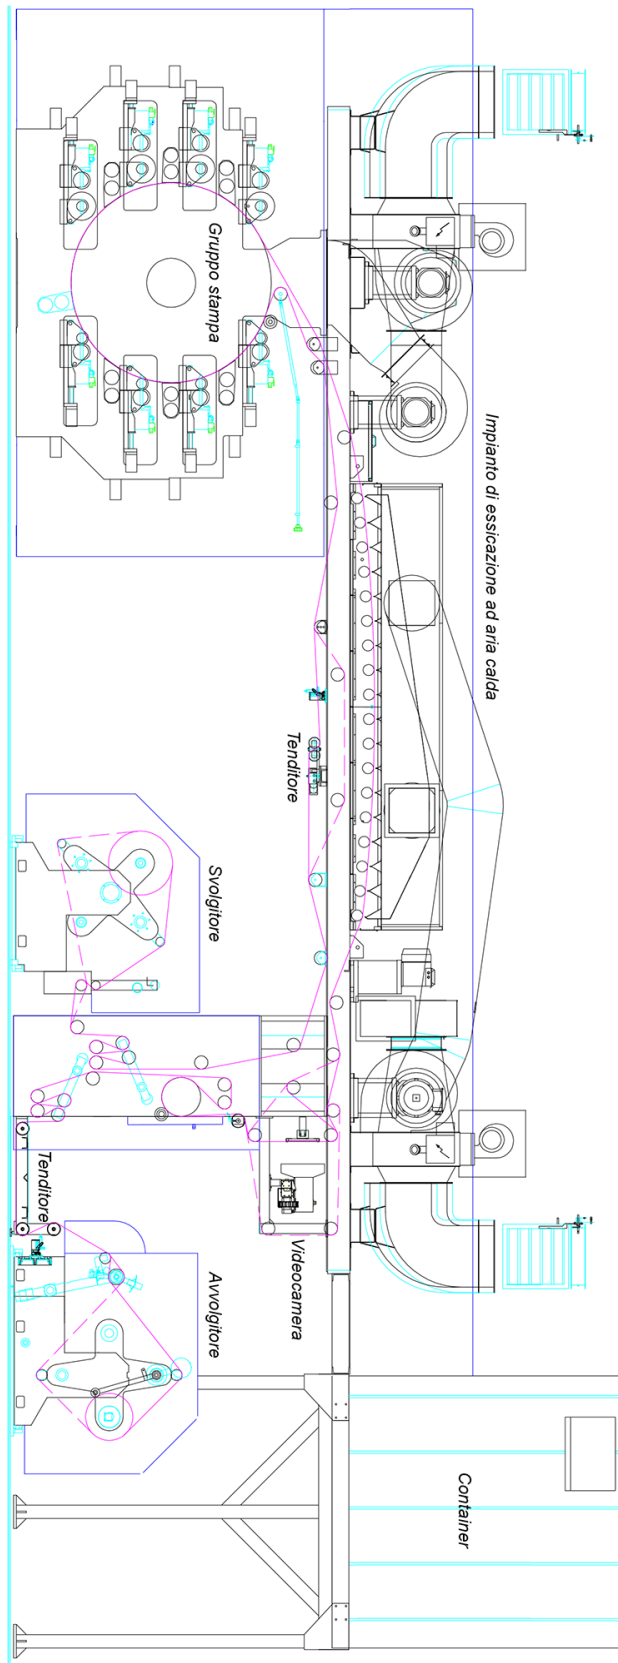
Disegno CAD di una macchina flessografica a tamburo centrale con 8 stazioni stampa.
